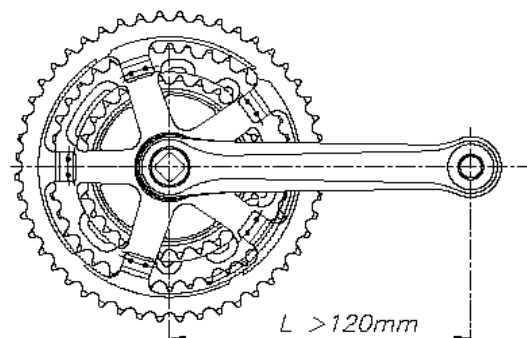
Dimensões de pedivela montada com engrenagem de bicicleta de uso adulto.
